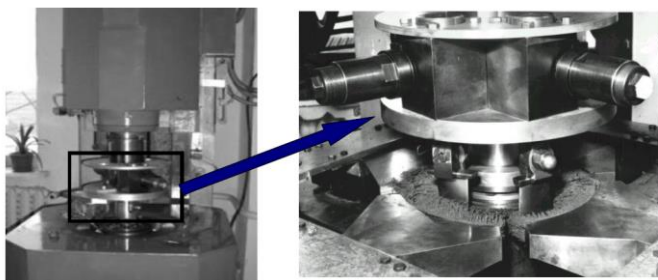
Внешний вид установки для МАО лопаток ГТД
